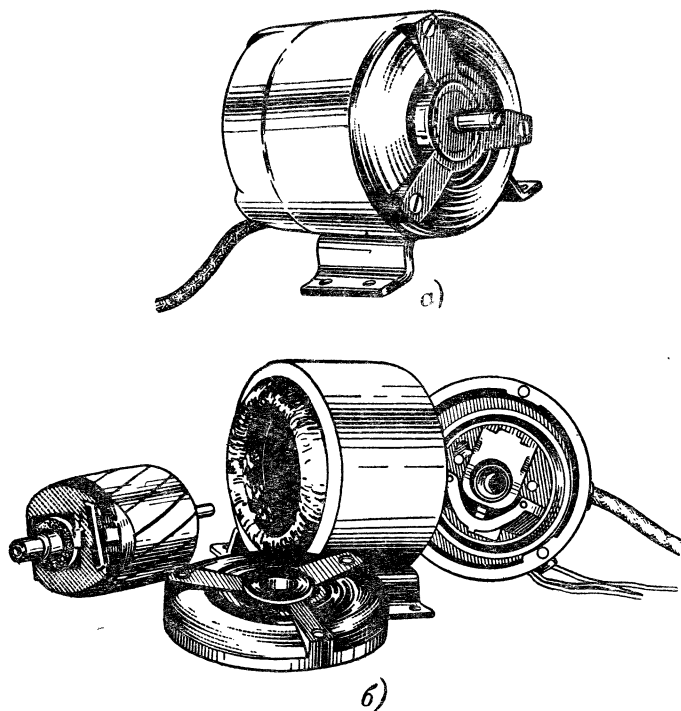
Закрытый двигатель типа 877-А для привода медицинских аппаратов.
